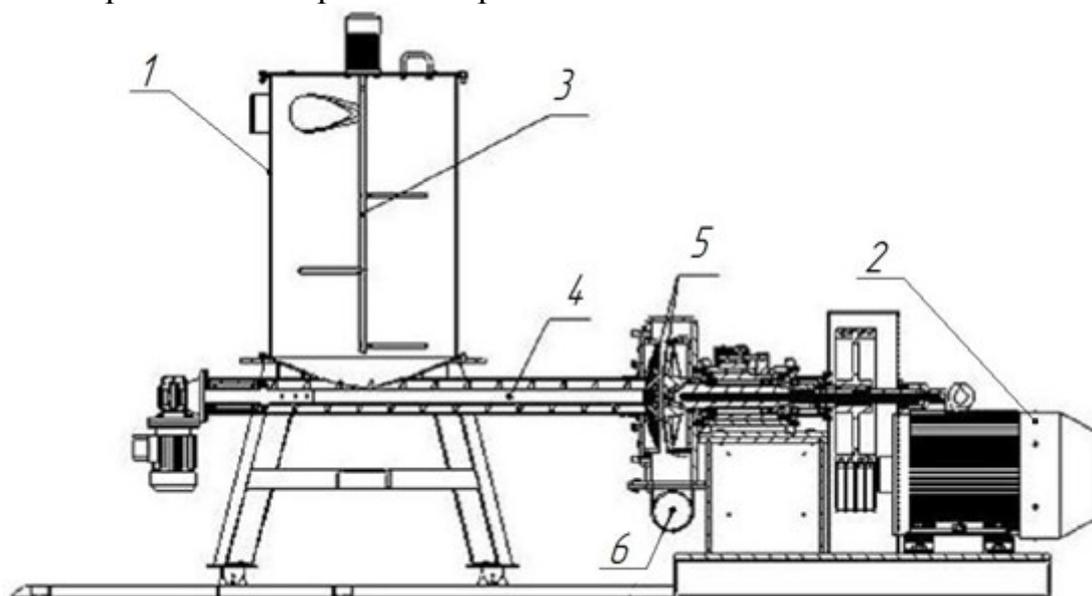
Пласткомпактор в разрезе: 1 – бункер; 2 – привод; 3 – ворошитель; 4 – винтовой питатель; 5 – роторный и статорный диски; 6 – фланец
